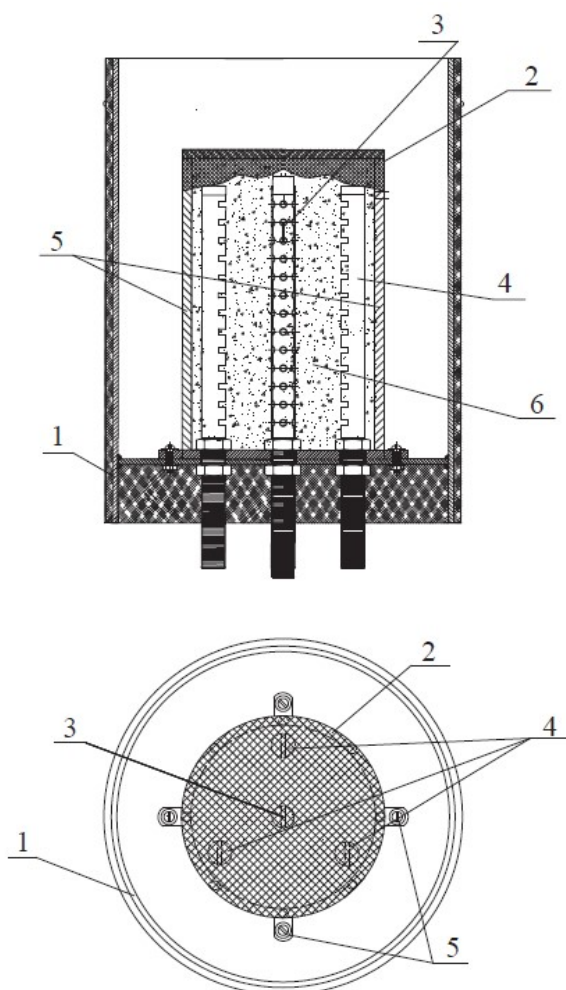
Конструктивная схема горелочного устройства: 1 – корпус; 2 – сетчатая насадка-излучатель; 3 – топливный инжектор; 4 – воздушные инжекторы; 5 – опорный каркас; 6 – рабочая зона
